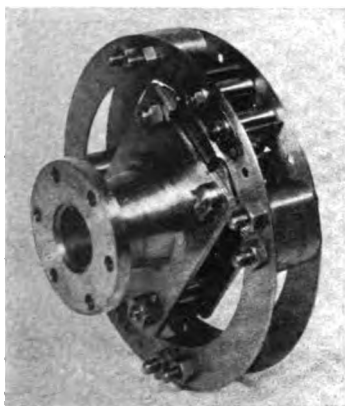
(links) Ansicht des Schwingers mit Befestigungsflansch.
